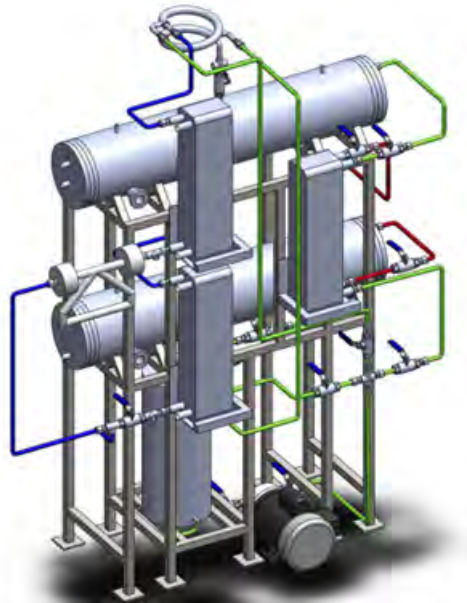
Distribución inicialmente planteada del sistema de absorción (Vista isométrica izquierda)
